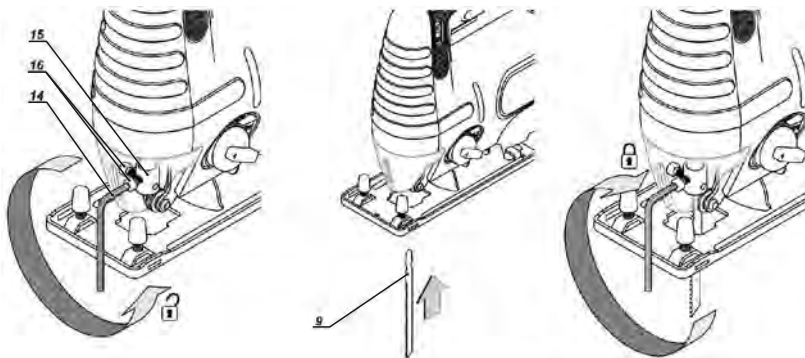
dibujo demostrativo del montaje y desmontaje de la hoja de sierra
